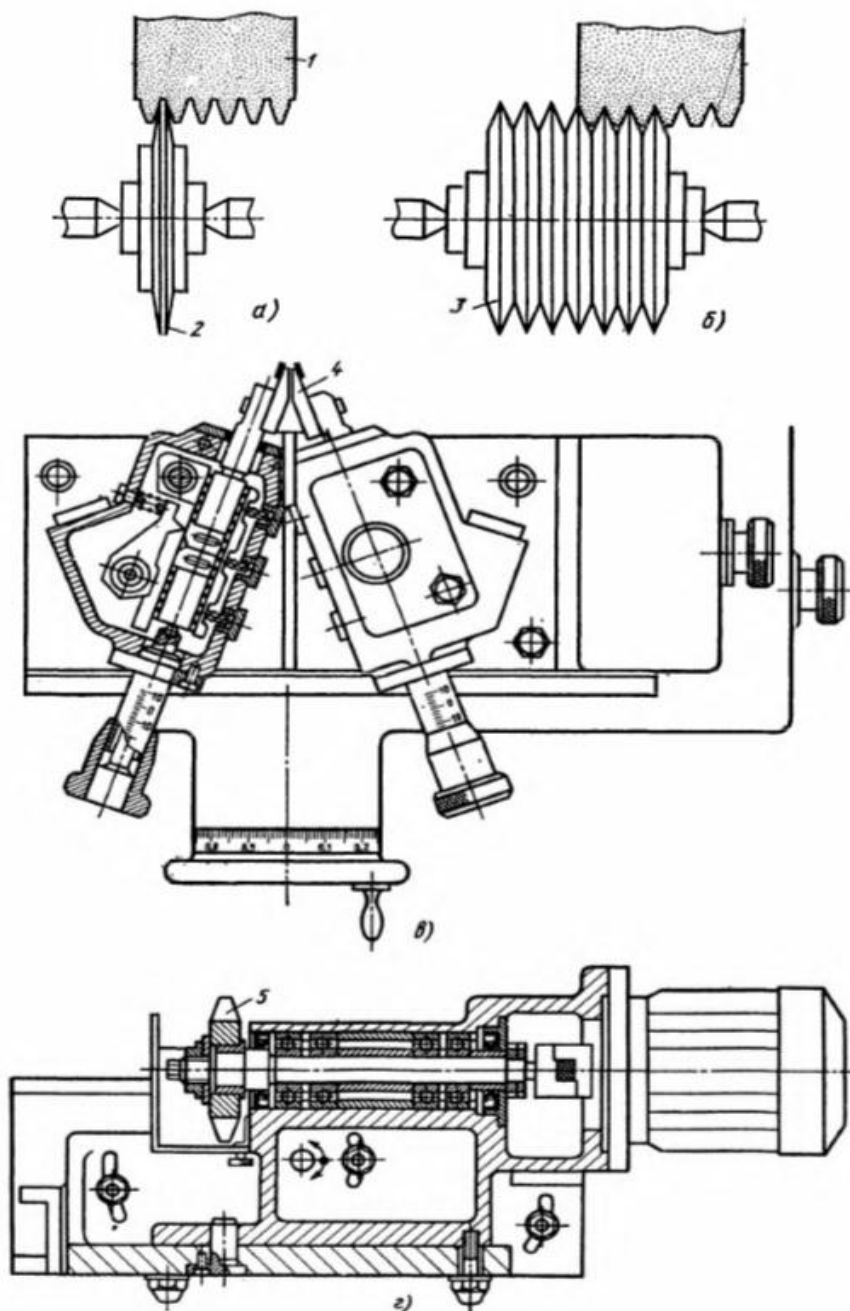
Правка черв'ячного абразивного круга: *а* – одновитковим накатником; *б* – багатовитковим накатником; *в* – алмазними різцями; *г* – алмазним роликом;
